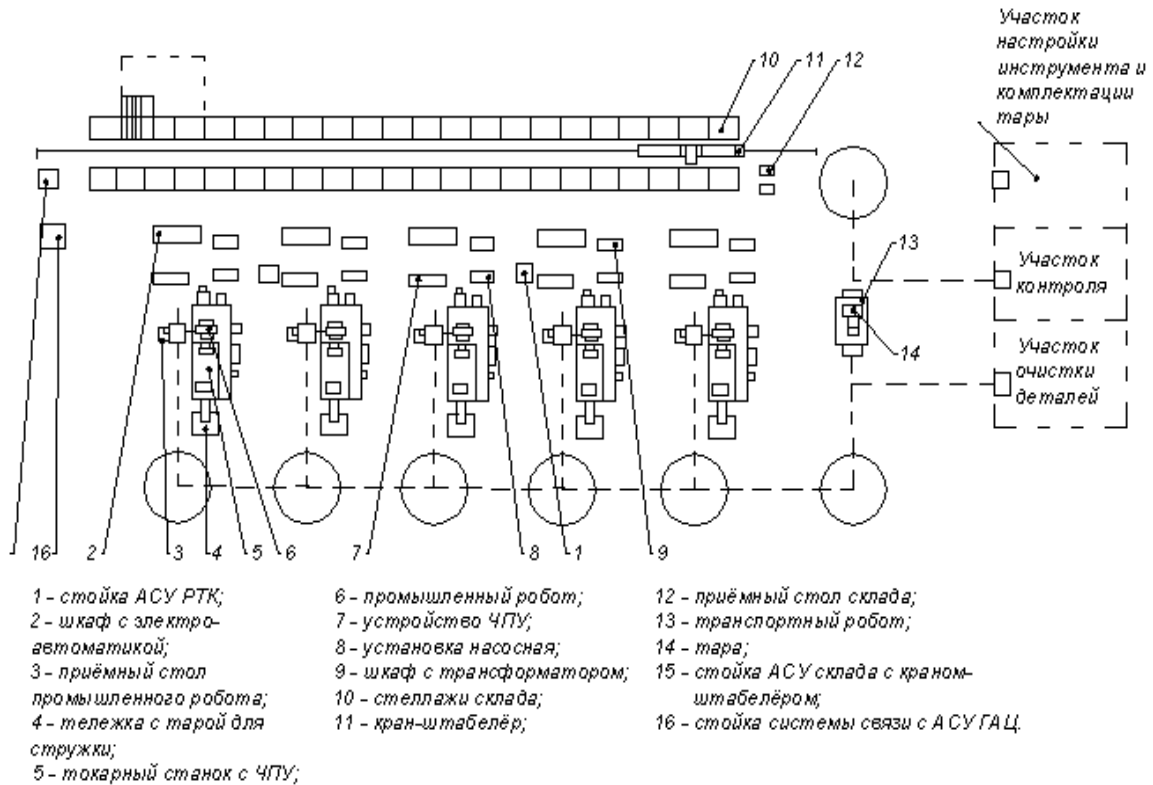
ГАУ и АТСС линейного типа и транспортным роботом для токарной обработки
